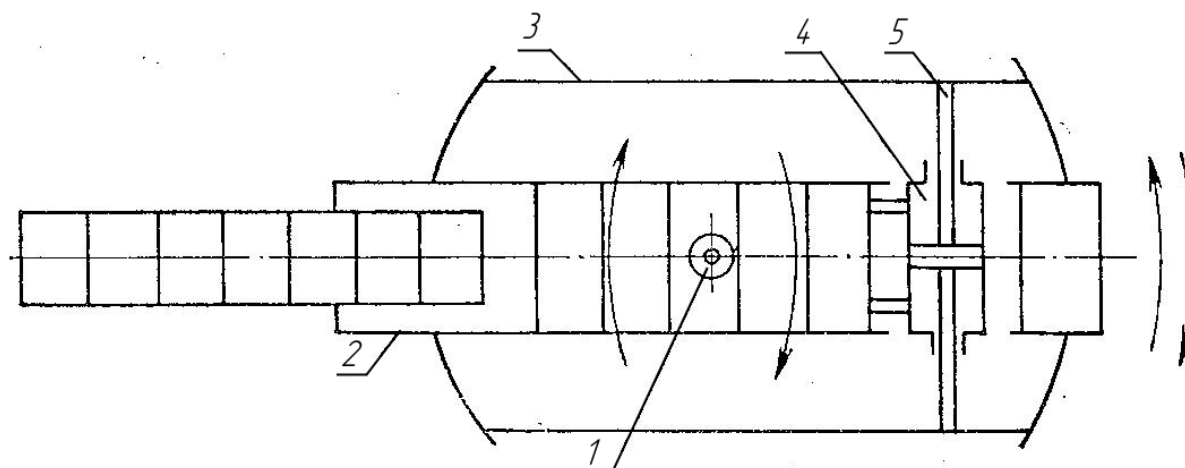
Принципова схема привода механізму бокового вирівнювання:
